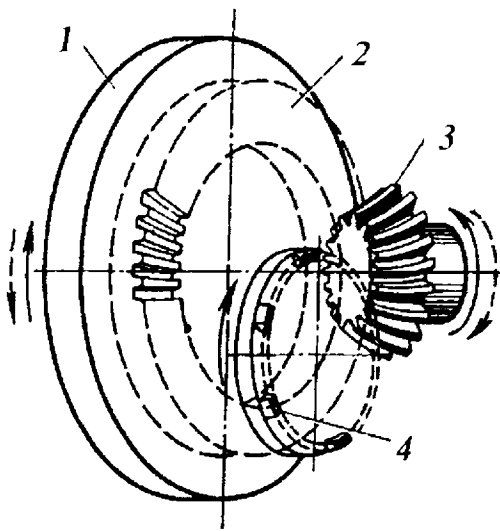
Нарезание конических колес с криволинейными зубьями: 1 – инструментальный барабан, 2 – воображаемое производящее колесо, 3 – нарезаемое зубчатое колесо, 4 – зуборезная головка с резцами
